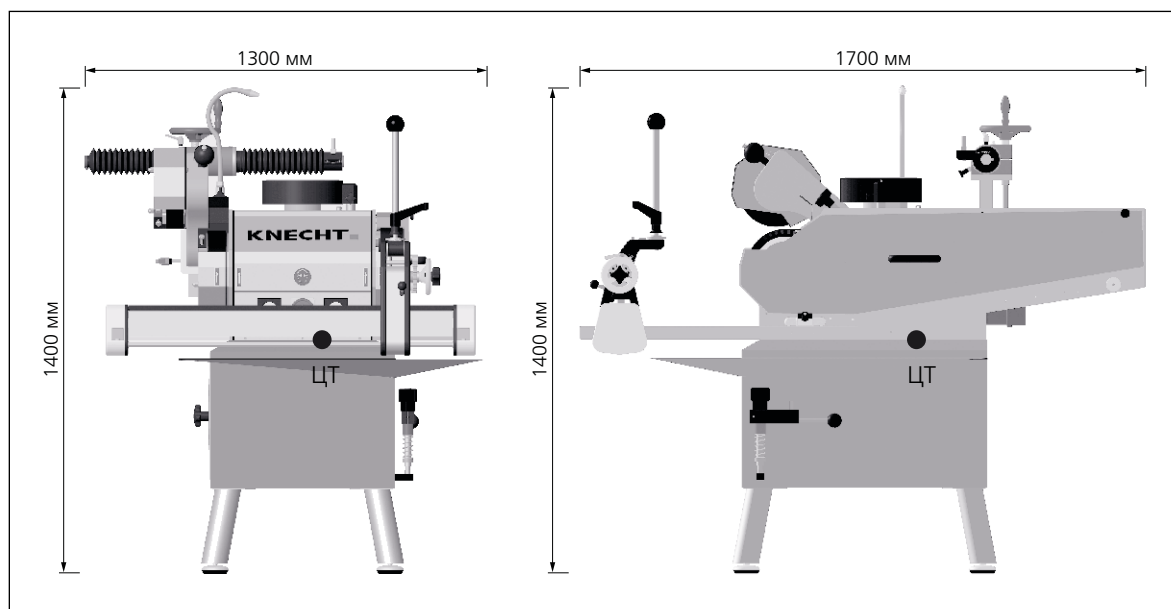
Размеры в мм и центры тяжести (ЦТ) станка S 20
